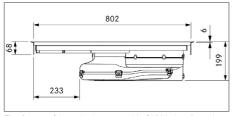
Dimensioni apparecchio PUXU vista frontale
